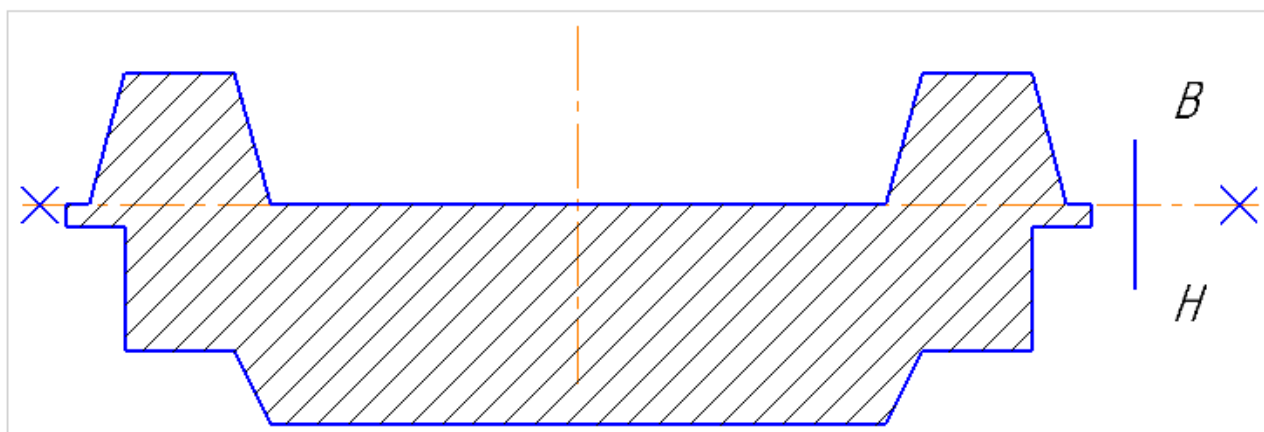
Схема отримання штампованої заготовки для деталі "Кришка підшипника "
